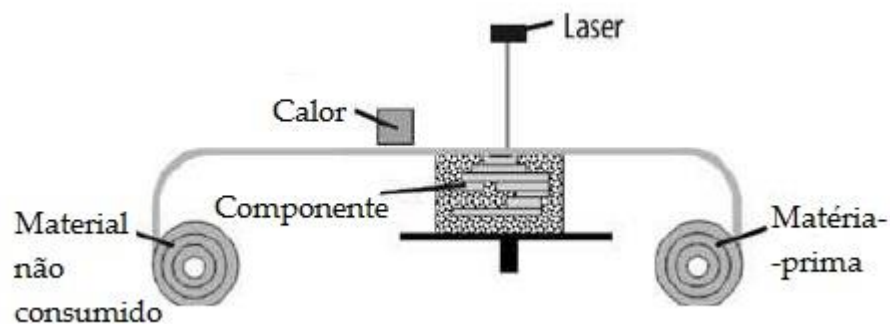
Esquema do equipamento de Sobreposição Laminar [11]
